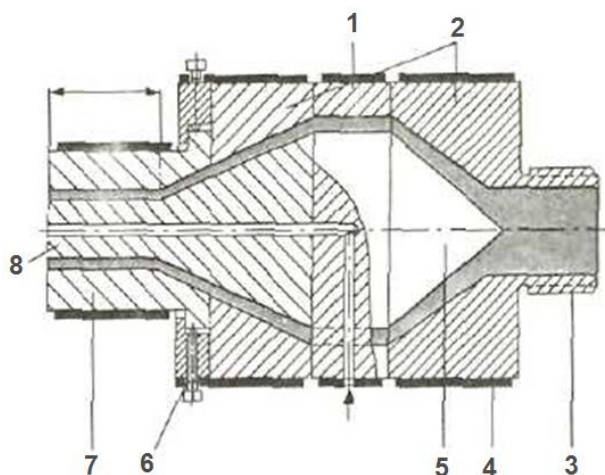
Дорн экструзионной головки для производства труб: 1 – держатель дорна; 2 – корпус; 3 – крепежный элемент; 4 – нагревательный элемент; 5 – наконечник дорна; 6 – центрирующий элемент; 7 – фильера; 8 – дорн.
